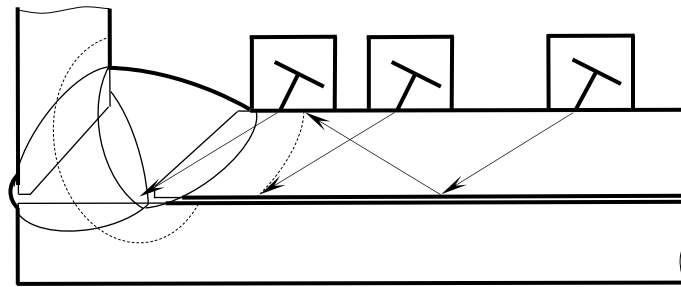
Схема контроля сварного соединения усиливающей накладки и углового сварного соединения тройника со стороны накладки
